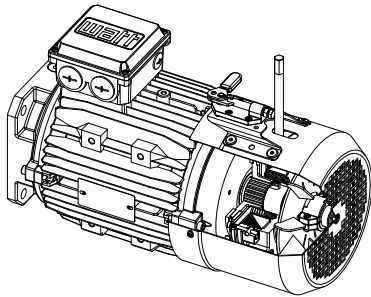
Handlüftung mit Arretierung (Bremse geschlossen)
